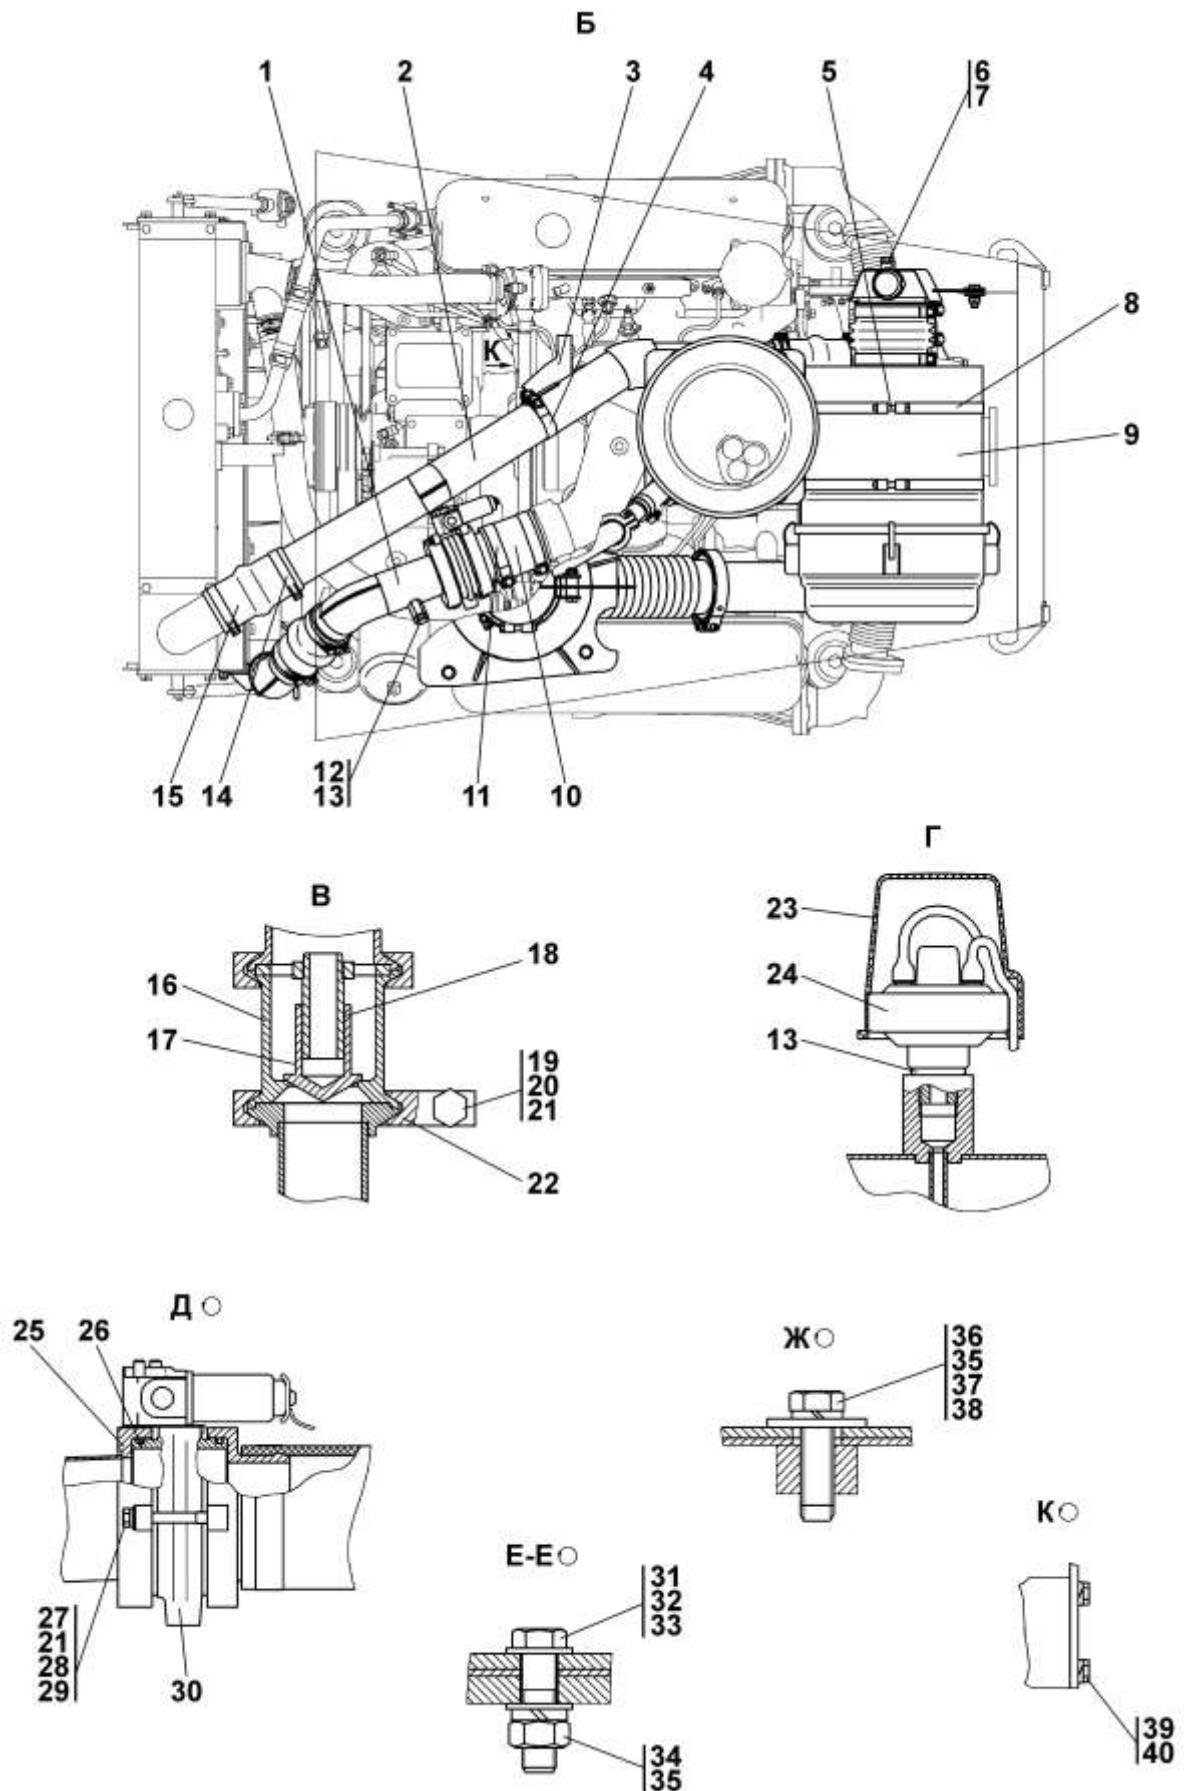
Установка системы воздухоочистки и выпуска
